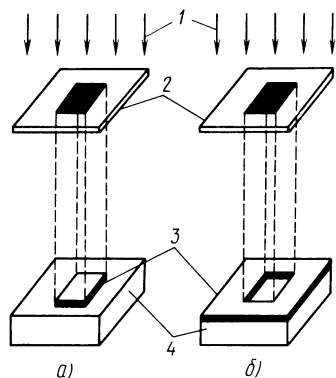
Схемы проявления позитивного (а) и негативного (б) фоторезисторов:
